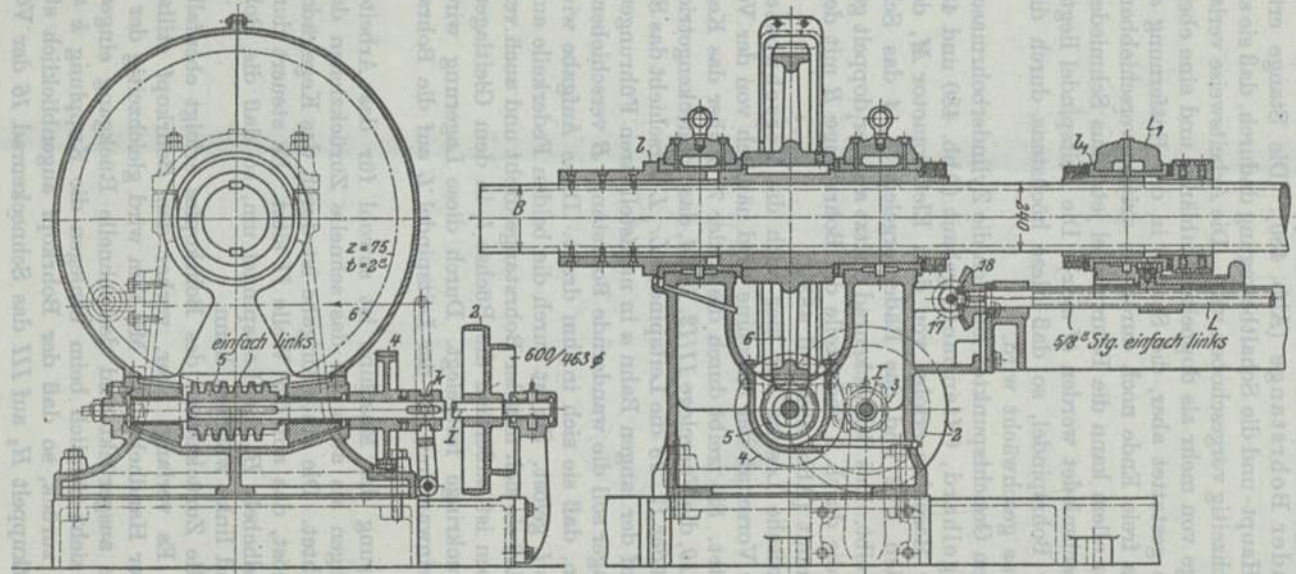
und 483. Antrieb der Zylinderbohrmaschine. Collet & Engelhard.
